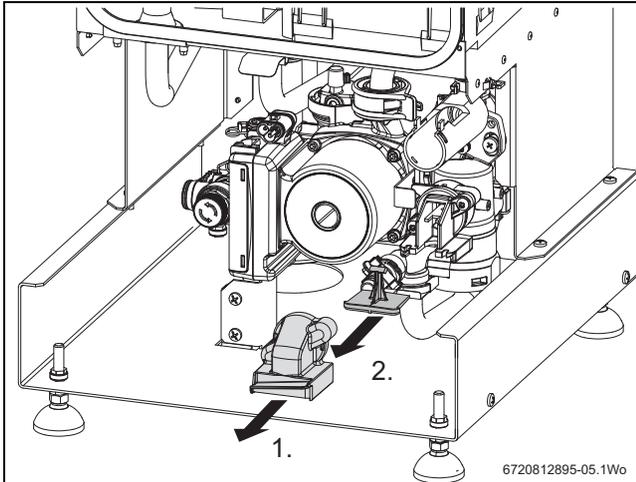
Entfernen der Steckscheibe für den Umschaltventilmotor
